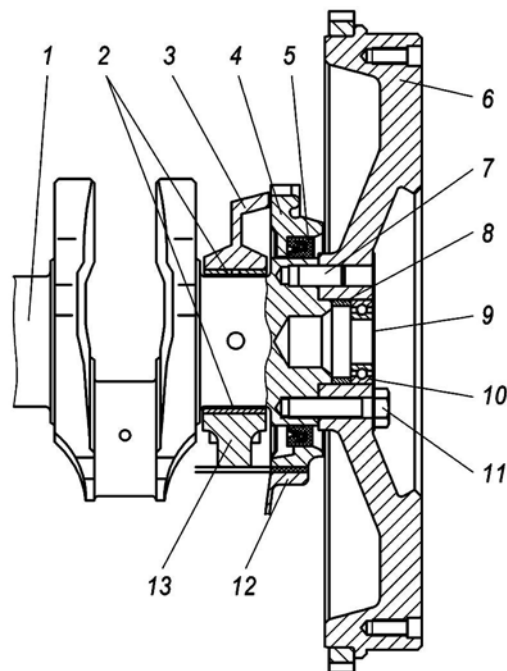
Задний конец коленчатого вала: 1 - коленчатый вал; 2 - вкладыши подшипника; 3 - блок цилиндров; 4 - крышка; 5 - манжета; 6 - маховик; 7 – установочный штифт; 8 - распорная втулка; 9 - шайба болтов маховика; 10 - подшипник; 11 - болт крепления маховика; 12 - масляный картер; 13 - крышка подшипника
